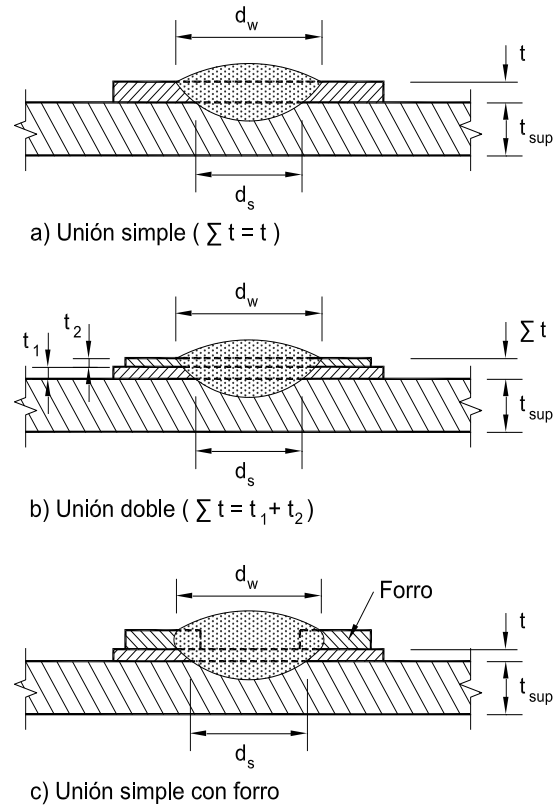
b. Posiciones de soldadura de arco por puntos
